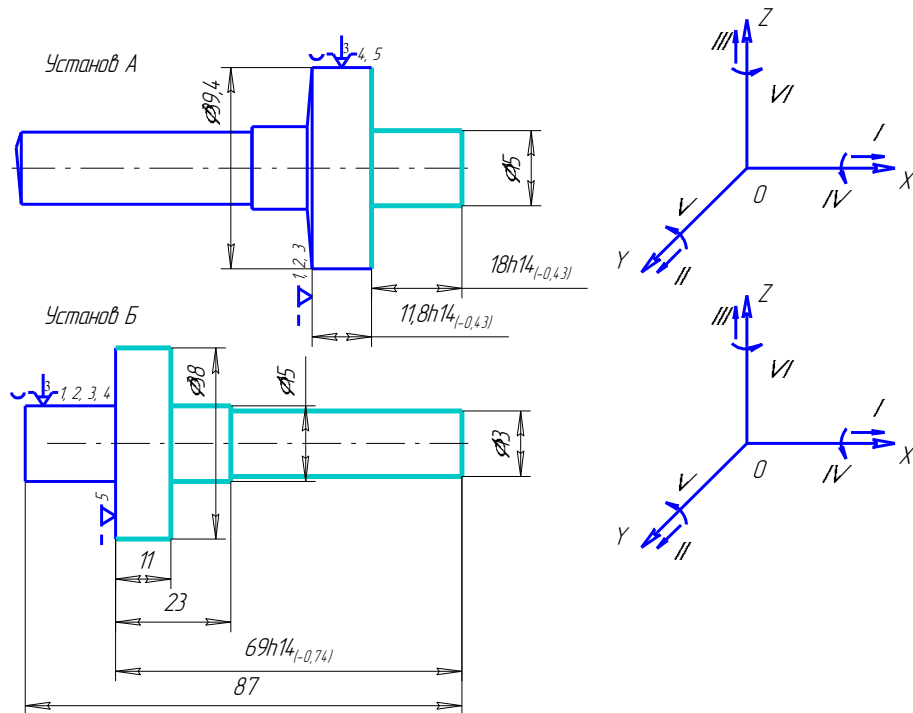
Базування заготовки на операції 015 за схемою №1
